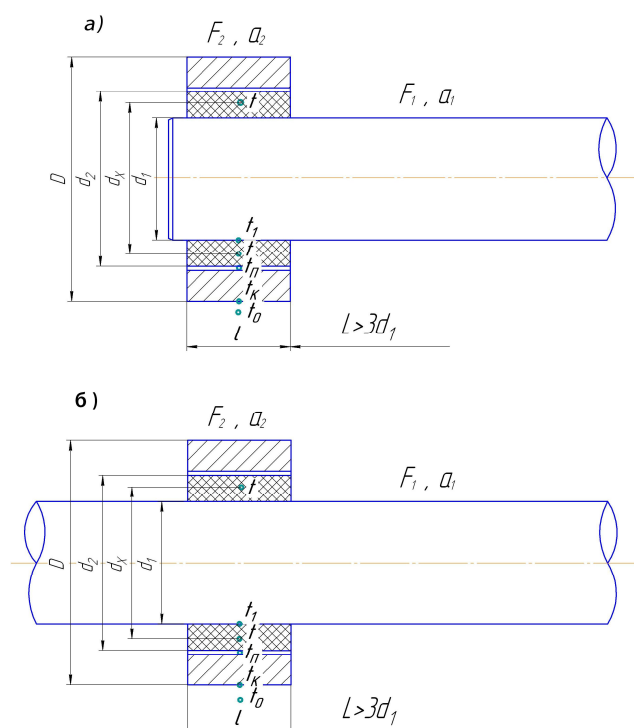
Схема подшипникового узла (обратная пара): а – концевой подшипник; б — срединный подшипник
